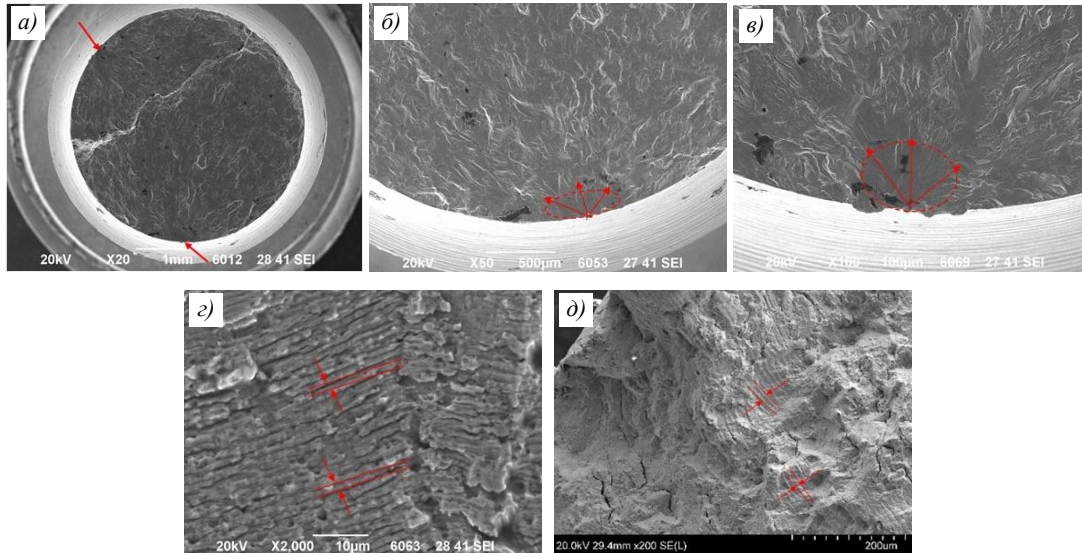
Общий вид (а) поверхности разрушения образца с надрезом С-типа: очаги разрушения (б, в), ширина усталостных бороздок перед зоной долома (з) и после очага разрушения (д)
